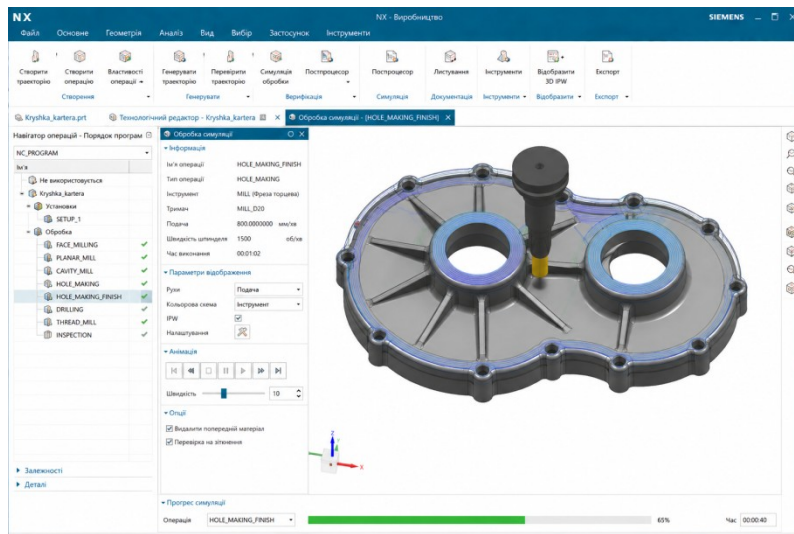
Чистова обробка отворів кришки фрезою
